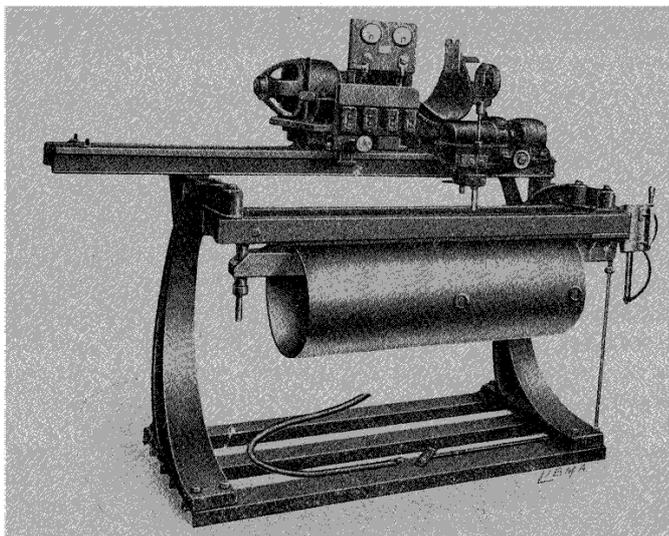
Machine automatique pour la soudure des viroles.
